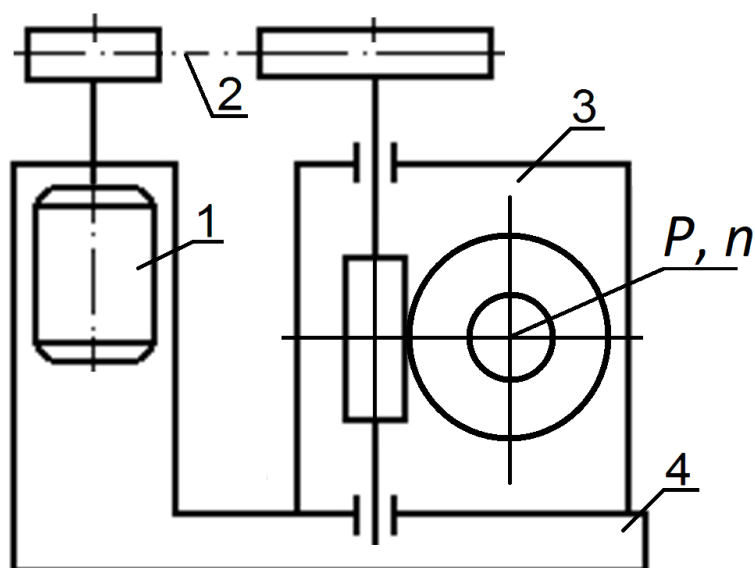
Привод качающегося подъемника: 1 – электродвигатель; 2 – горизонтальная клиноременная передача; 3 – червячный редуктор; 4 – сварная рама
